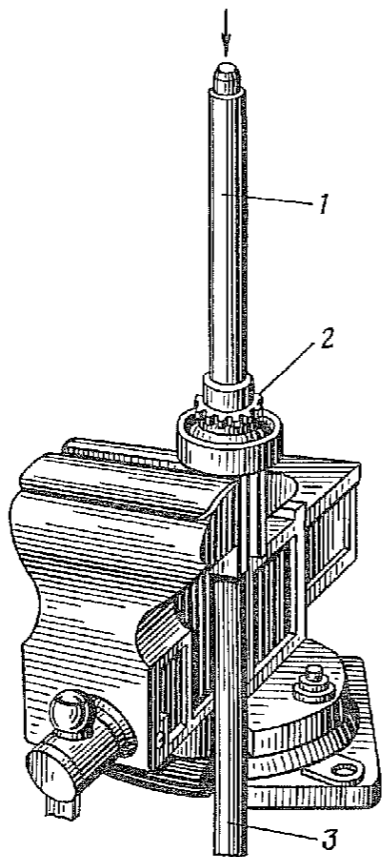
Спрессовка и напрессовка зубчатого хвостовика в сборе с подшипником:
